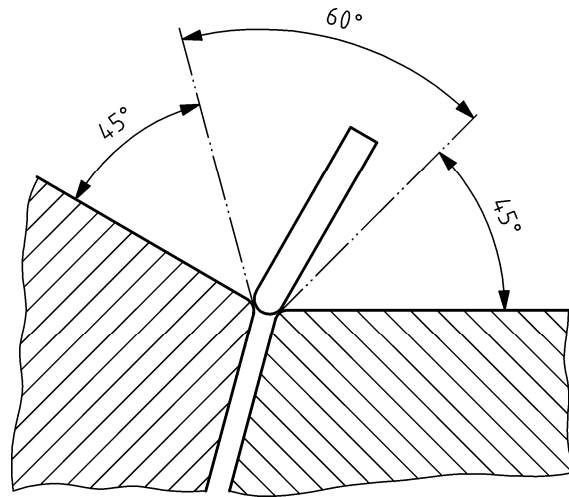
Bewegung des Rundstabs mit 8 mm Durchmesser
